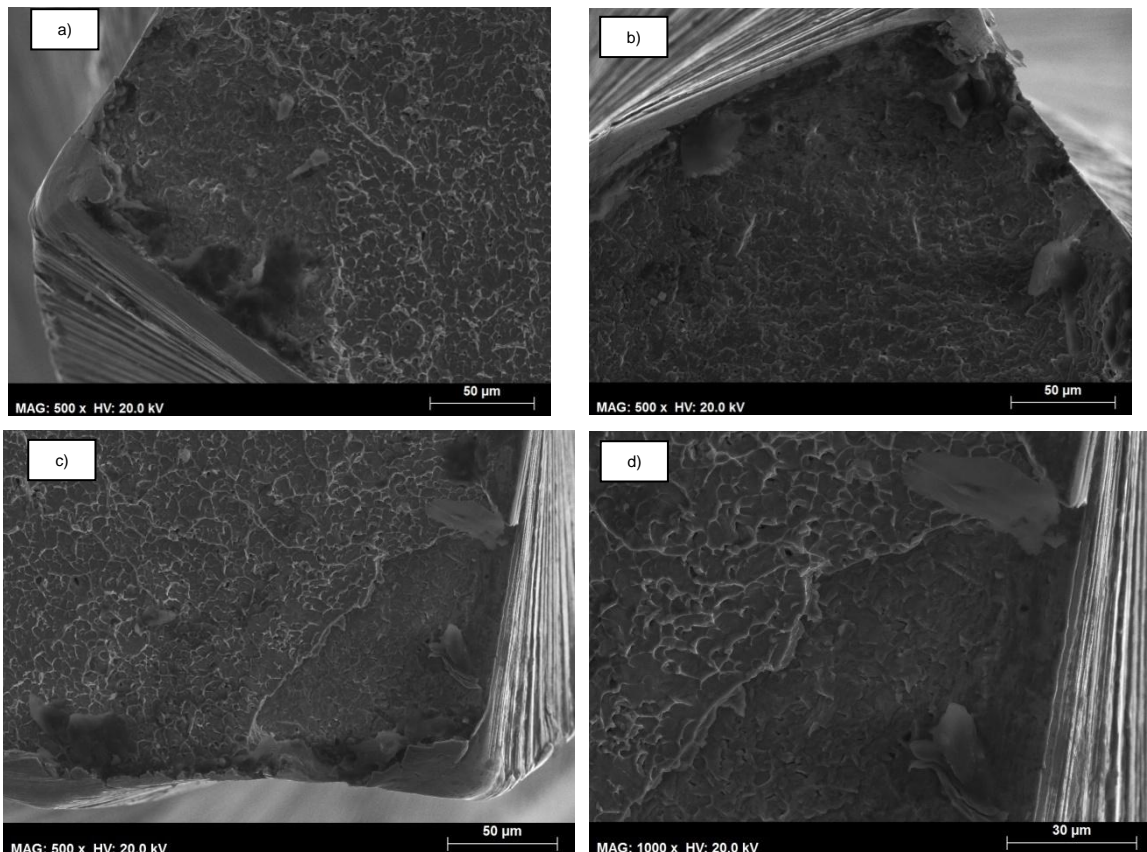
Fissuração múltipla no instrumento 025.08\_1.
